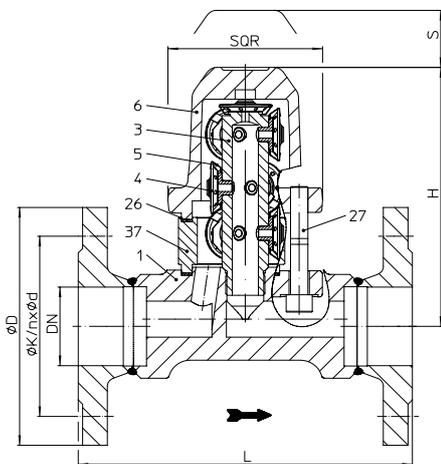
1....10K2 (DN40-50) com 10 cápsulas, com flanges
